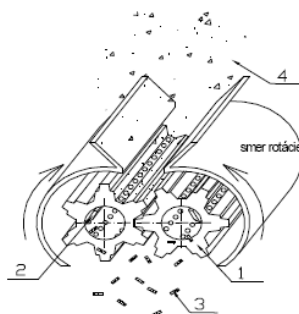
konstrukce je shodná s předchozím typem. Rozdíl je v lisovacím nástroji. Výhodou tohoto stroje je jednodušší konstrukce. Nevýhodou vyšší tření mezi nástrojem a maticí (rychlejší opotřebení rotoru). [3]
